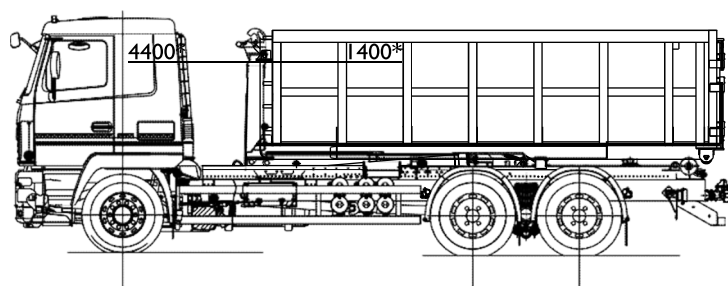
Внешний вид МАЗ-6950С5-11040000-001
